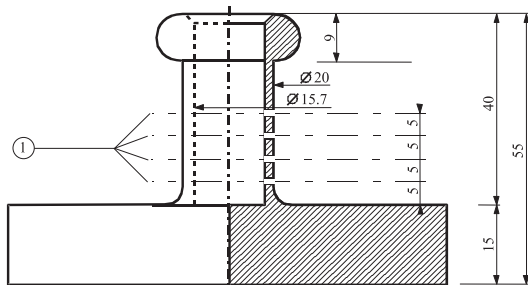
Полый бронзовый цилиндр, закрытый с одной стороны; чертеж и размеры детали в мм
